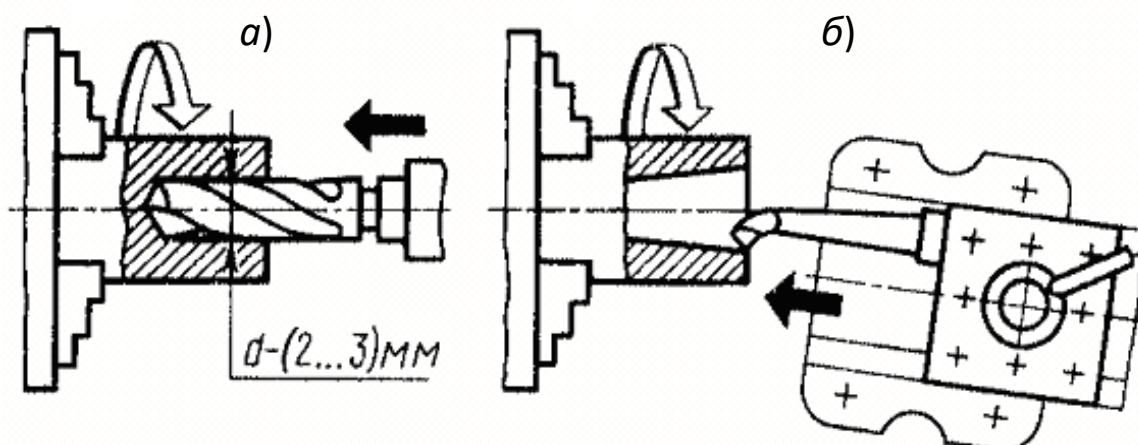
Обработка внутренней конической поверхности способом поворота верхней части суппорта:
